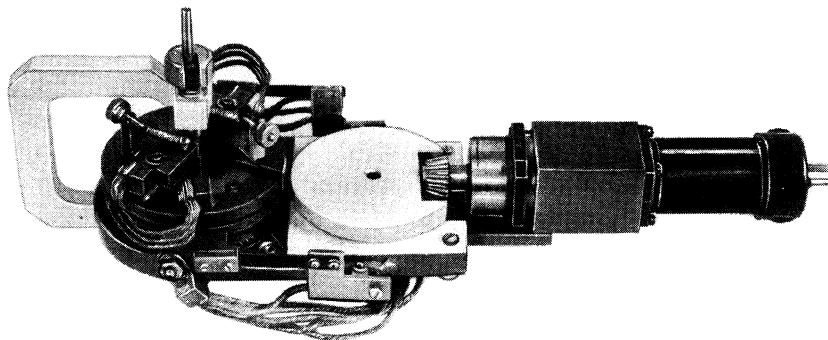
Сварочная головка Н-159 для сварки трубок диаметром 3...6 мм
